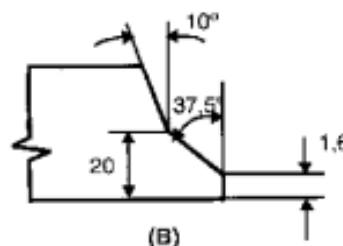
Geometría de la unión con soldadura de aluminio.
